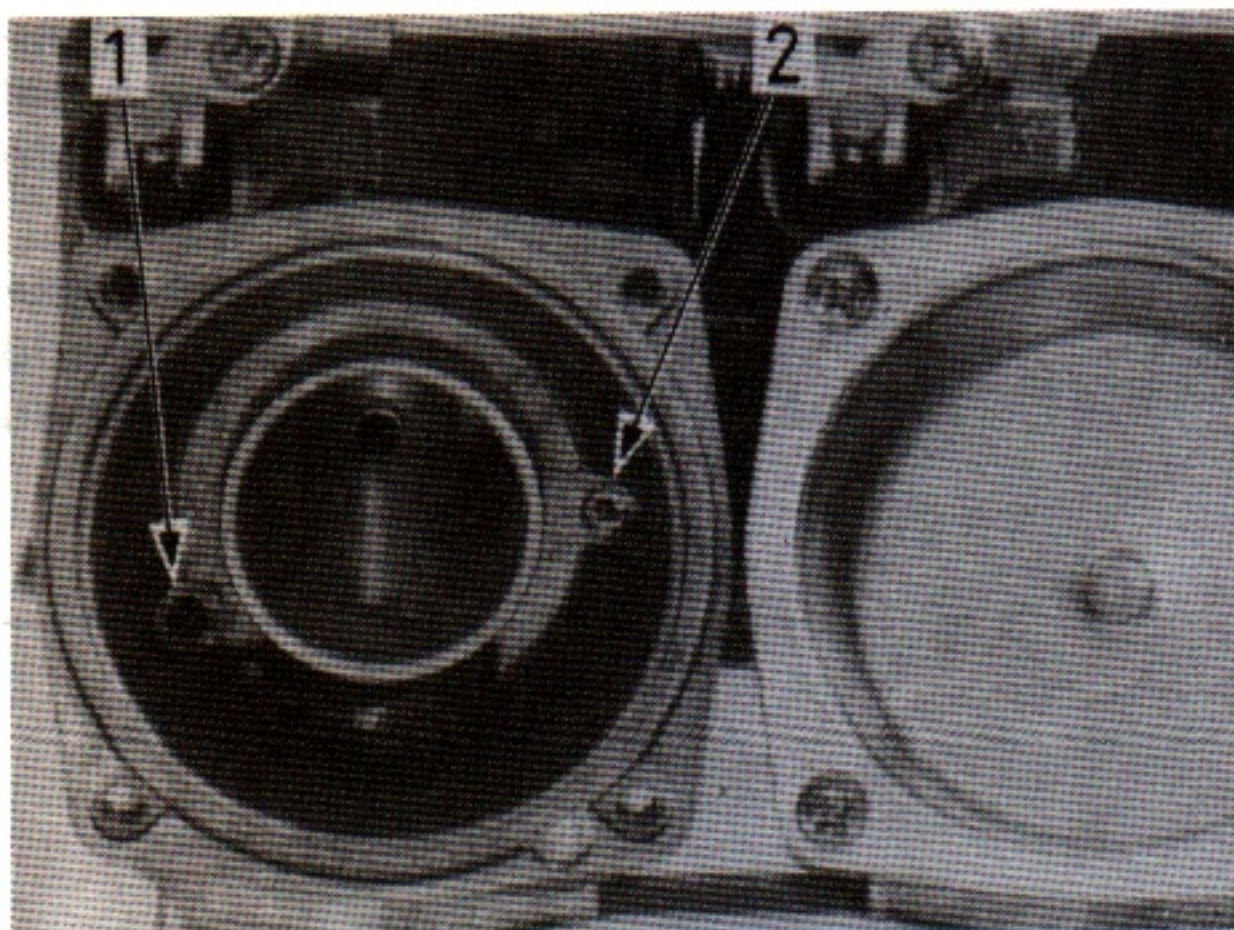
Una vez desmontada la corredera con su membrana el cuerpo del carburador muestra este aspecto. 1, pasaje de aire para equilibrado de la membrana; 2, surtidor de aire de la marcha lenta.
